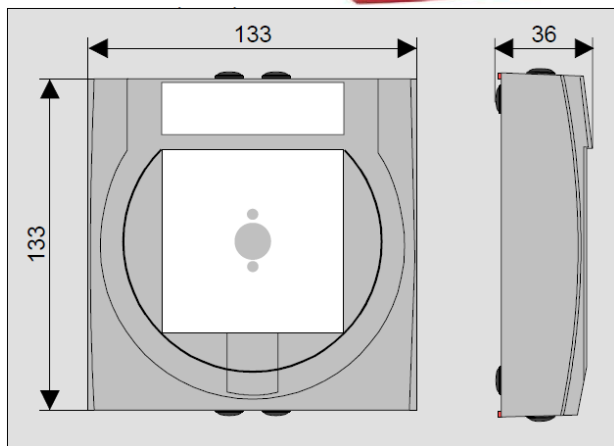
Ручной извещатель в большом корпусе (в сборе)
